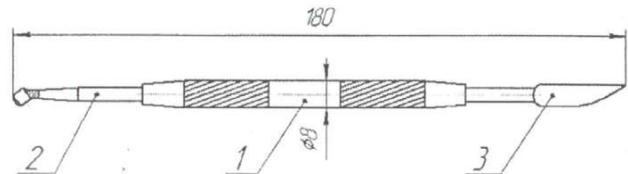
Чертеж ножа-корректора 1-ручка-держатель, 2-резец, головка, 3-нож.
